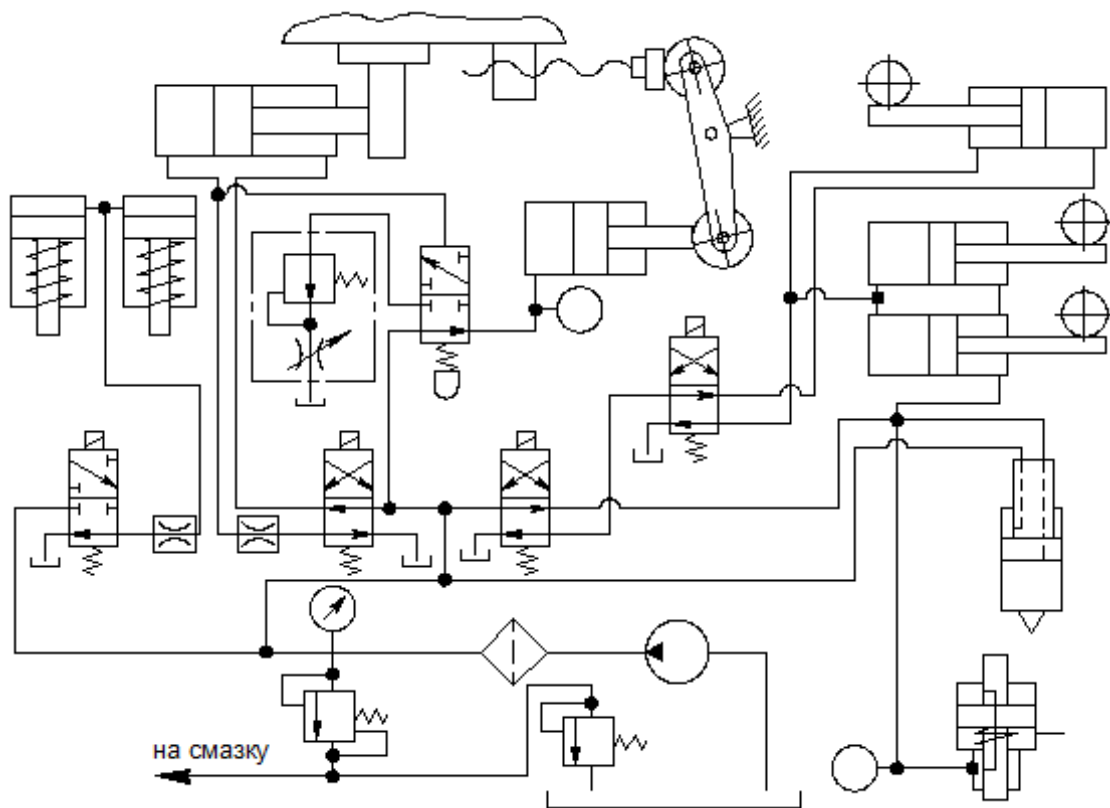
Гидравлическая схема фрезерного станка мод. 5А312
